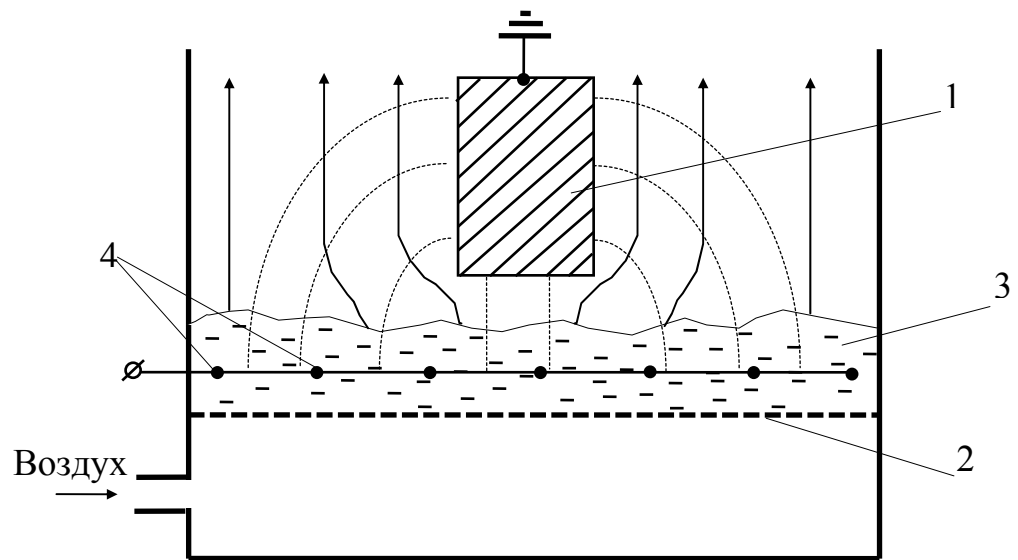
Нанесение покрытия в камере с кипящим слоем.
